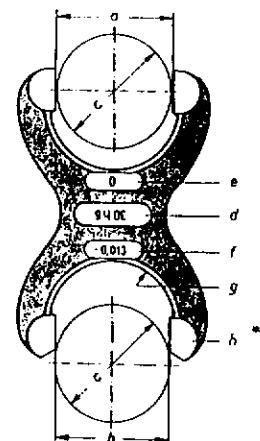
Designaciones en calibres de herradura: a) medida máxima D_g lado bueno (lado de «pasar»); b) medida mínima D_k lado malo (lado de «no pasar»); c) medida real del árbol, menor que D_g y mayor que D_k ; d) medida de ajuste; e) diferencia superior; f) diferencia inferior; g) capa de pintura roja; h) mordazas o garras de medida, achaflanadas (g y h caracterizan al lado de no pasar o lado malo).
